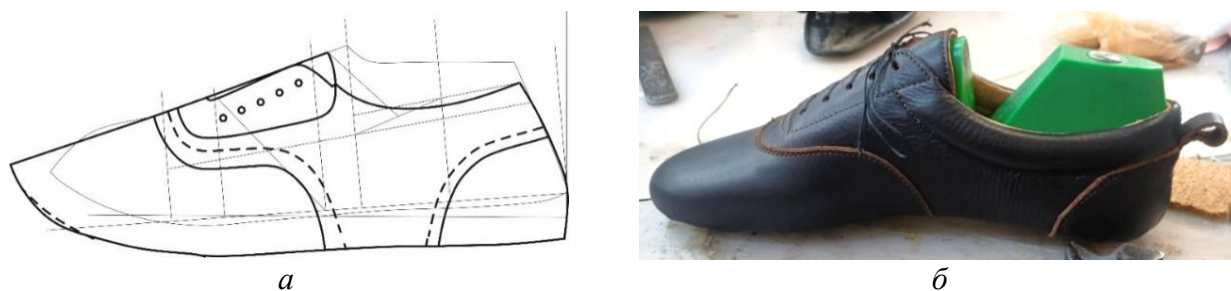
Чертеж конструктивной основы (а) (разработано автором), заготовка полуботинка с настрочной союзкой, на танцевальной колодке (б) (фото: асп. Бурцев А.И., рук. Карасева А.И.)
